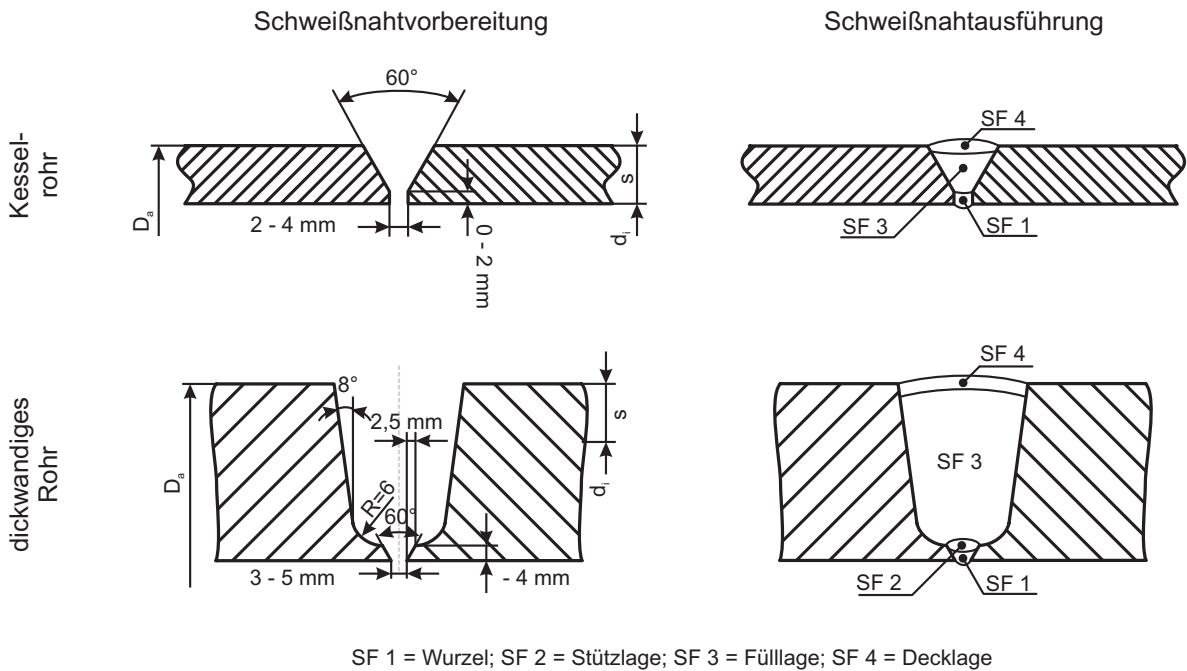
Schweißnahtvorbereitung und Schweißnahtausführung der ausgeführten Schweißungen (siehe auch [Tabelle 5.1](#))
